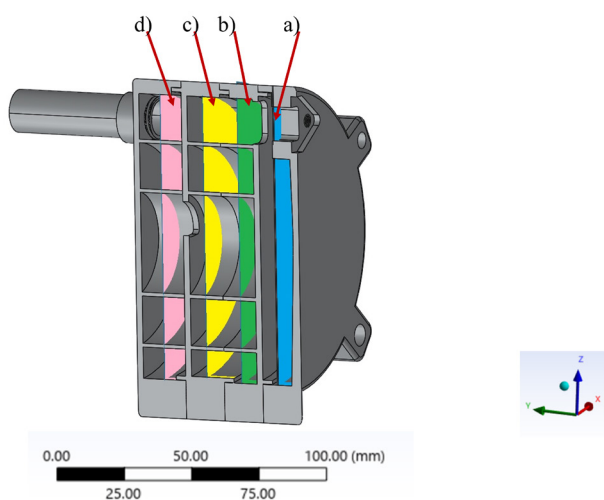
Vista de los planos xz del silenciador: (a) plano 1; (b) plano 2; (c) plano 3; (d) plano 4.
